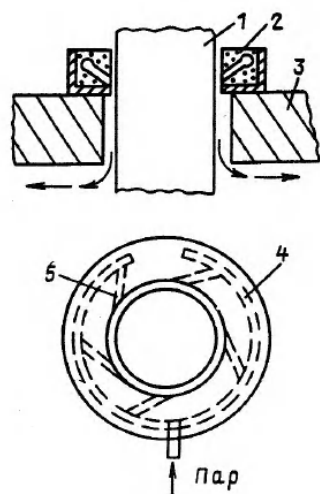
Схема струйного газодинамического уплотнителя электродных отверстий: 1 — электрод; 2 — керамический уплотнитель в металлическом корпусе; 3 — свод; 4 — кольцевой коллектор; 5 — сопла
